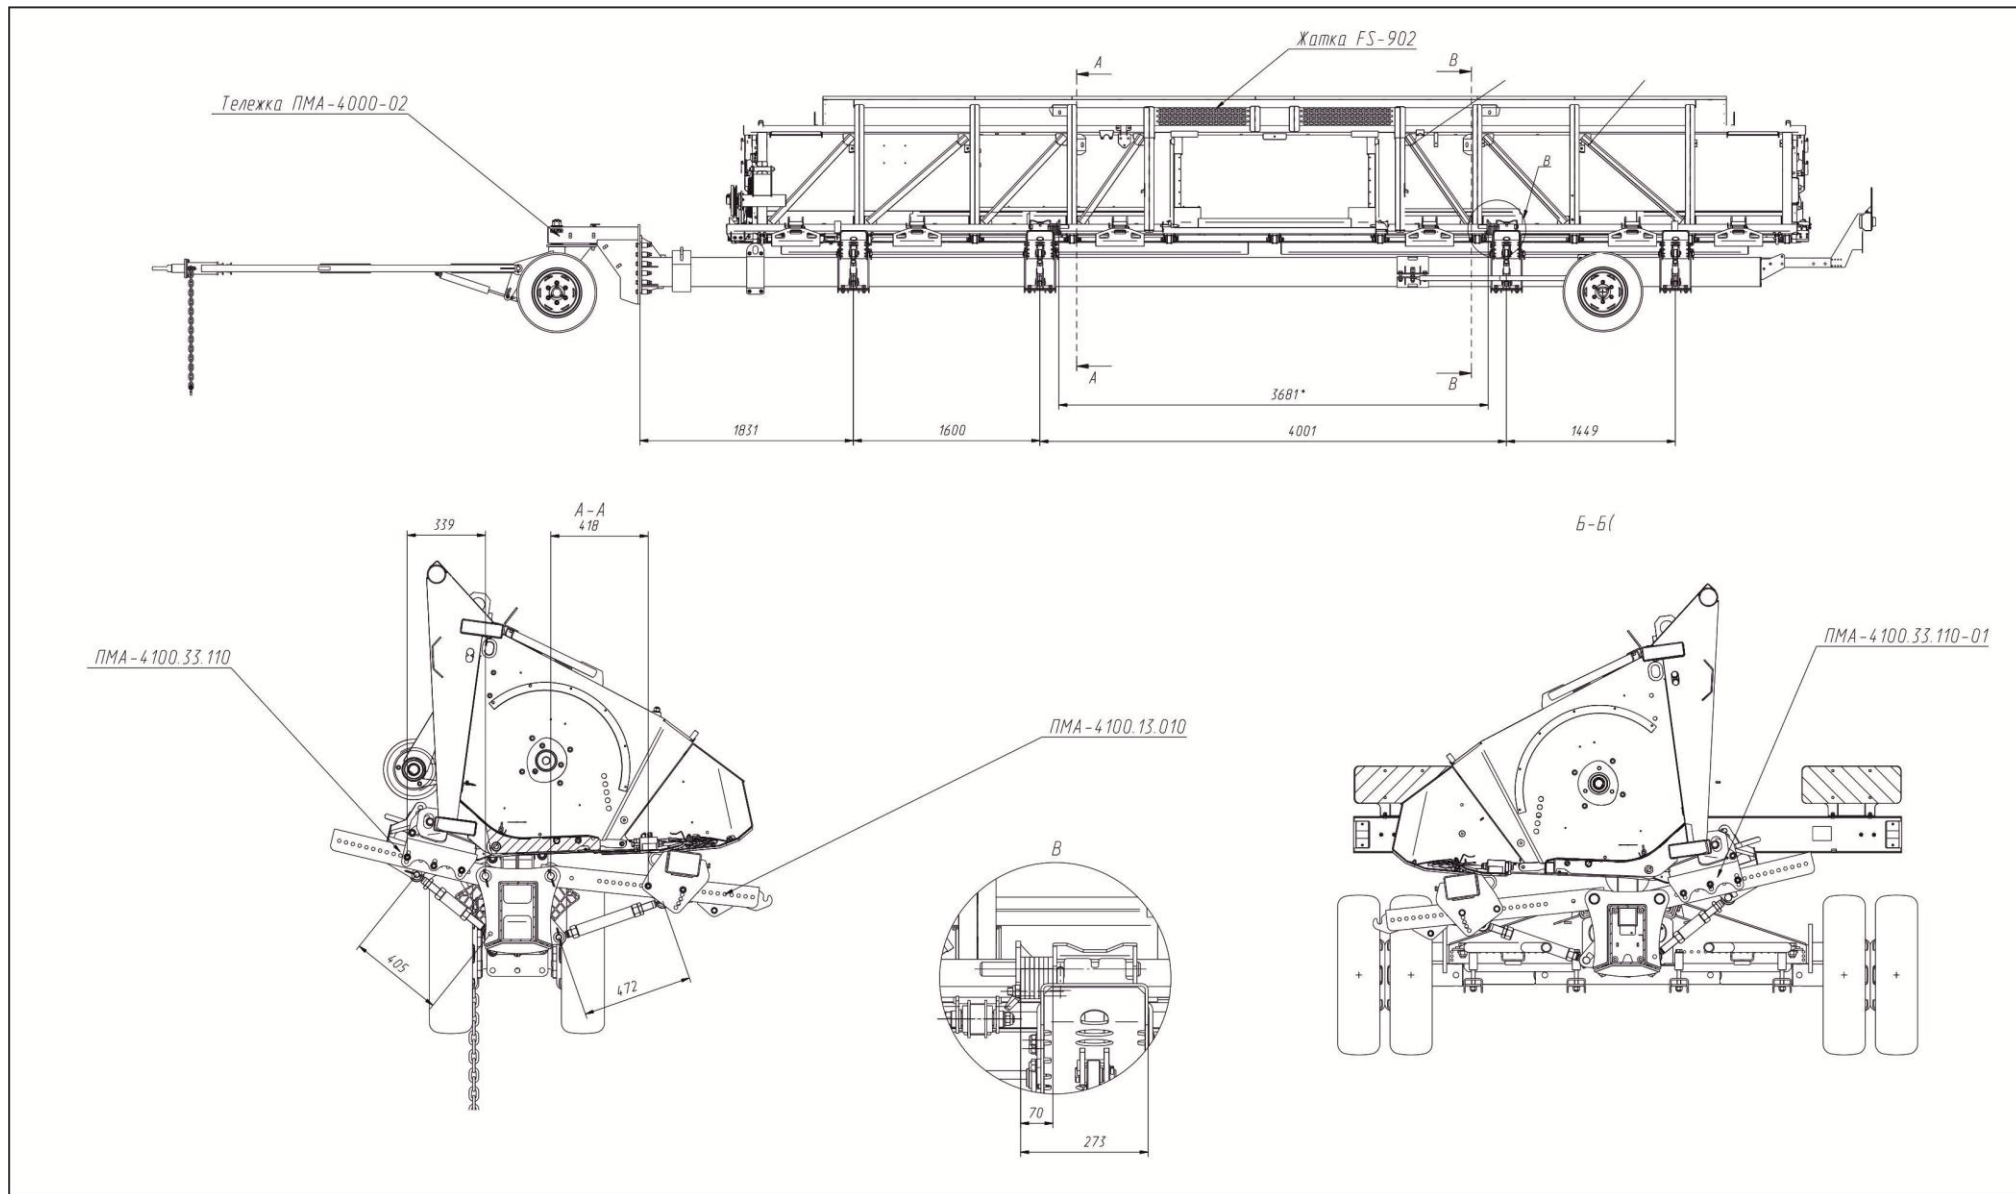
Схема установки жатки на приспособление ПМА-4000-02
